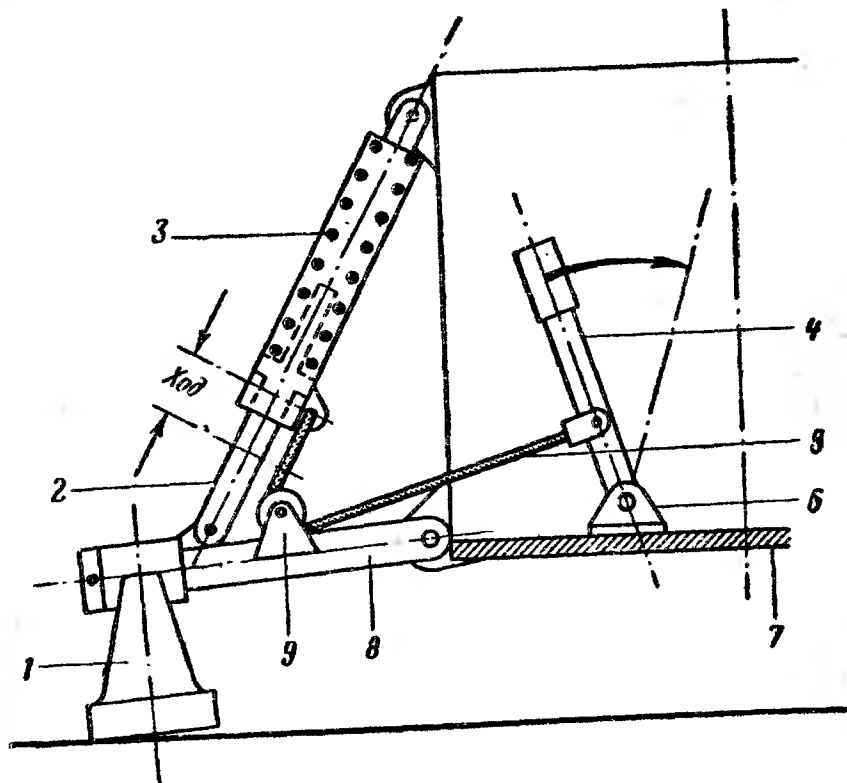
Схема приспособления для страгивания аэросаней: 1 — лыжа; 2 — амортизационная стойка; 3 — пружина; 4 — рычаг раскачки машины; 5 — трос; 6 — узел крепления рычага; 7 — пол аэросаней; 8 — полусось; 9 — ролик.
